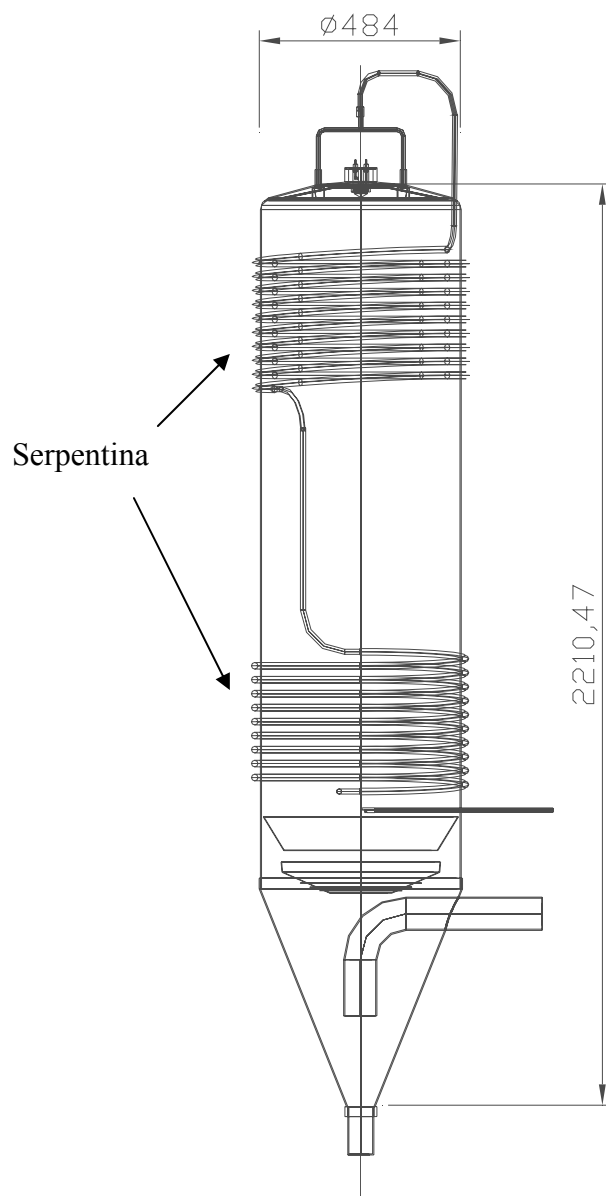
Esquema geral, em CAD, da serpentina de aquecimento do ar de secagem.
